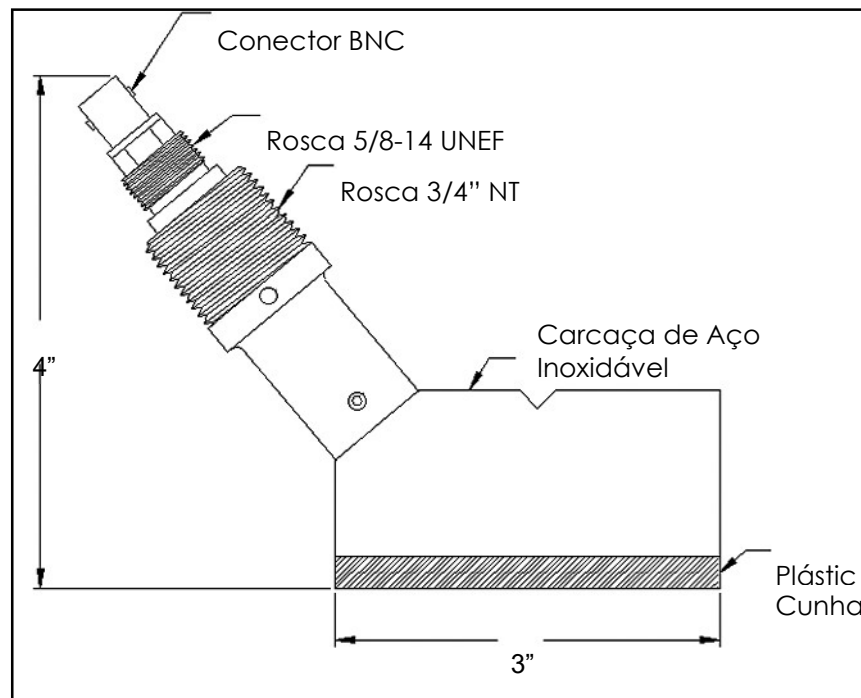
Conjunto do Transdutor (Des. de ref. 752-163)
